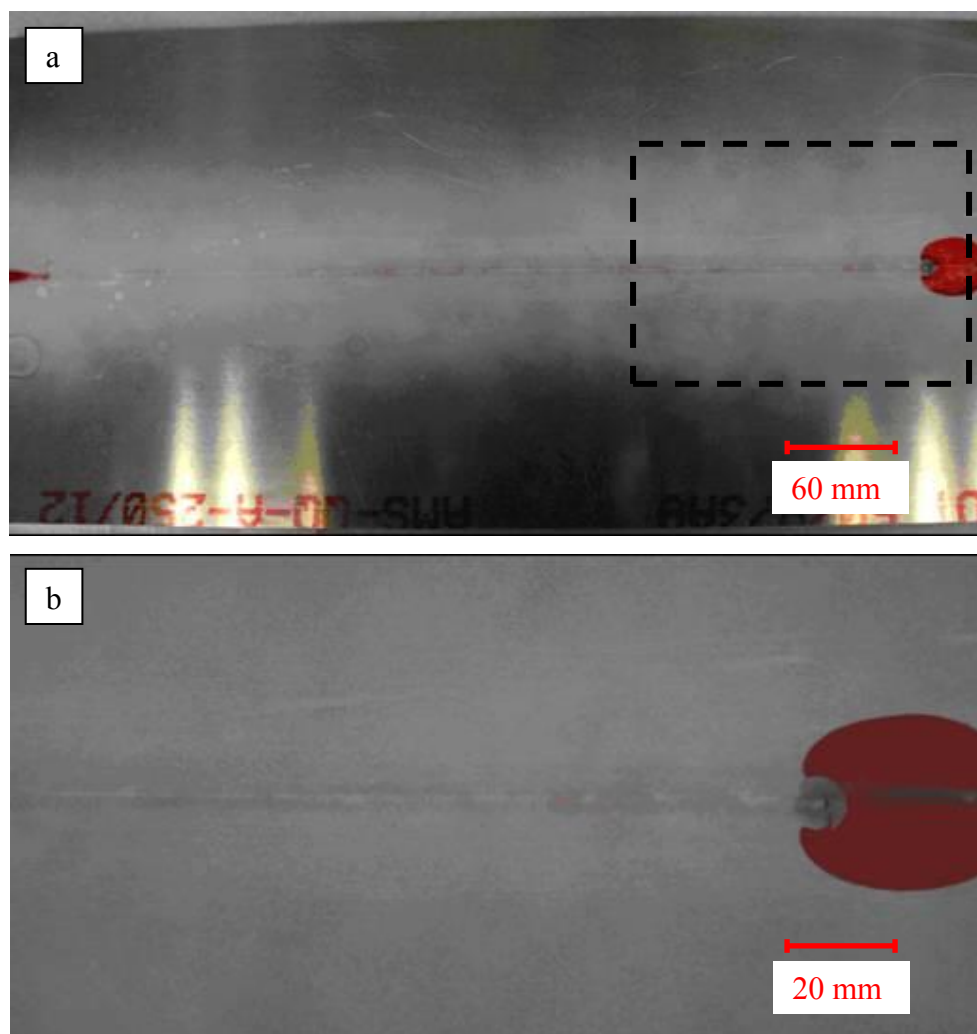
(a) Inspection par liquide pénétrant de l'échantillon soudé en appliquant une force verticale de 11 kN. (b) Élargissement de la partie du joint à l'extrémité non soudée de la plaque.
